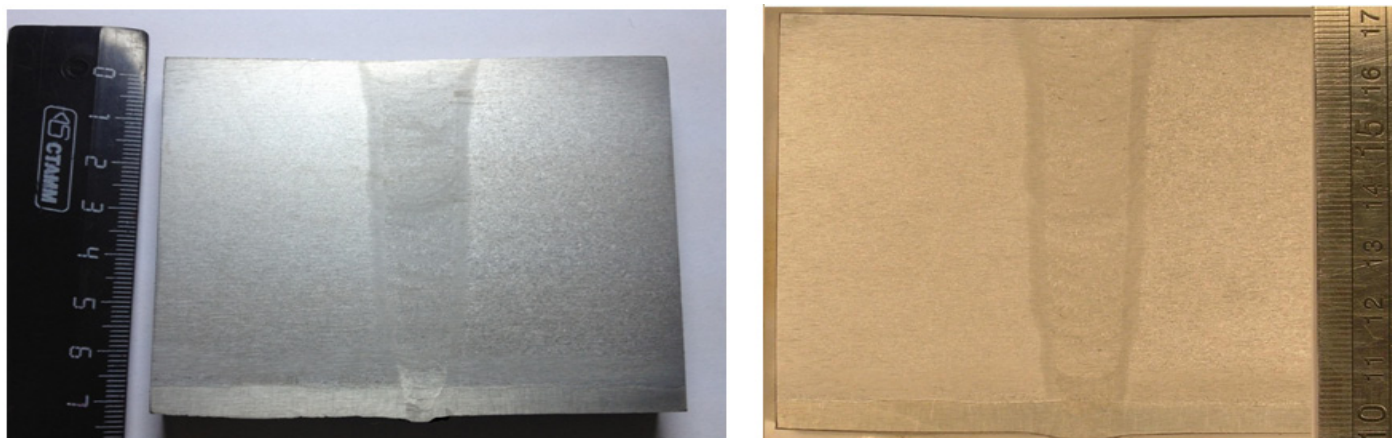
Макроструктура сварных соединений макетов №1 и №2
